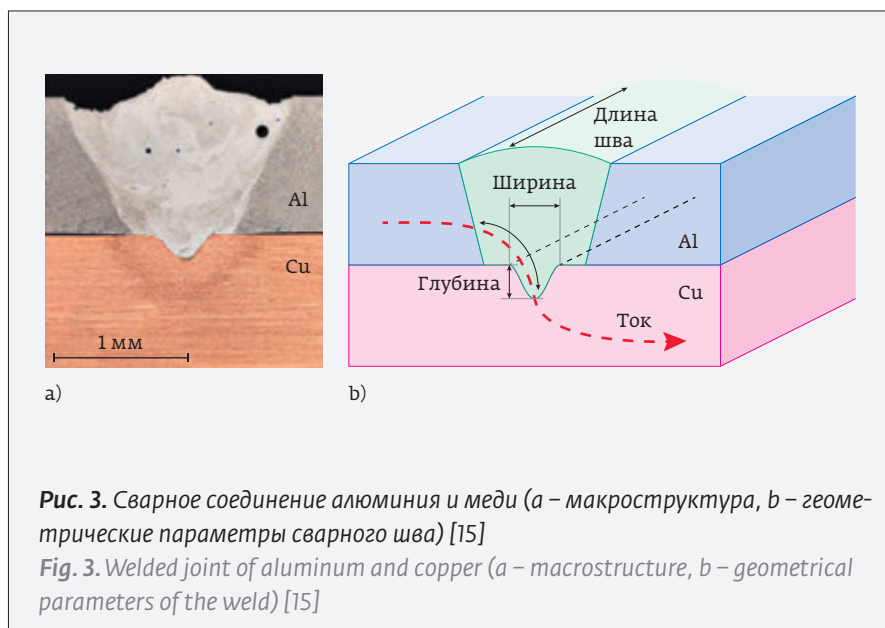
Сварное соединение алюминия и меди (а – макроструктура, б – геометрические параметры сварного шва) [15]
